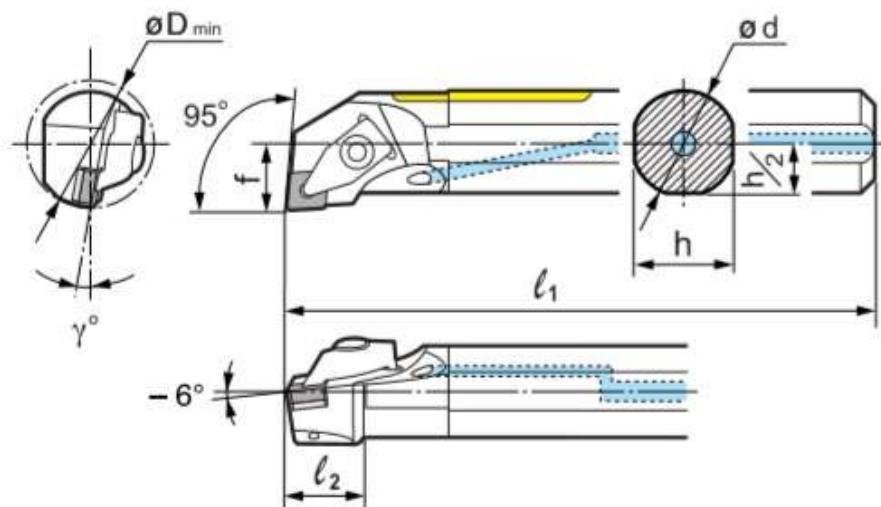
Державка Sumitomo для обработки внутренних поверхностей
